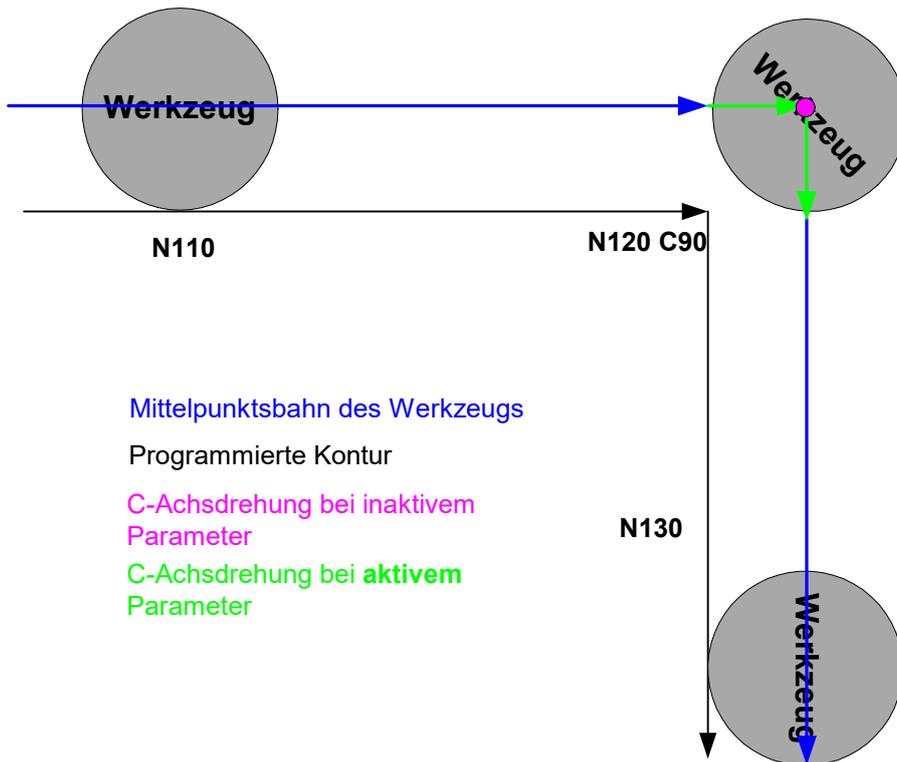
Prinzipieller Bewegungsablauf einer C-Achse mit G25
